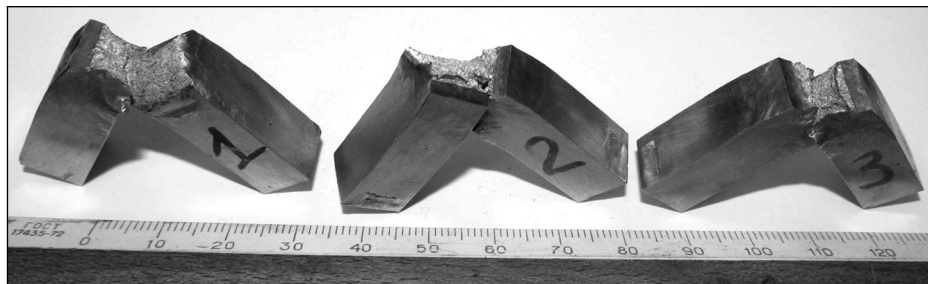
Образцы металла модельного двухслойного слитка из стали 316 после исследований на ударный изгиб (KCV)
